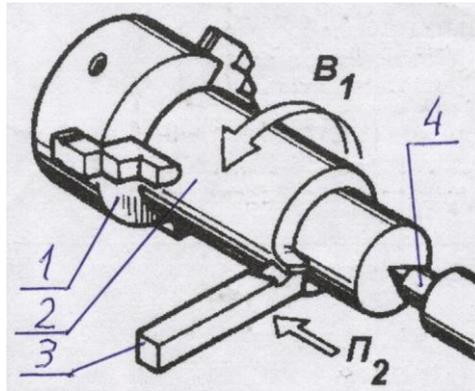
Схема продольного точения: 1 – зажимной самоцентрирующий патрон; 2 – обрабатываемая заготовка; 3 – резец; 4 – задний центр для поджима заготовки к патрону; V_1 – главное движение – вращение заготовки; P_2 – продольная подача резца
